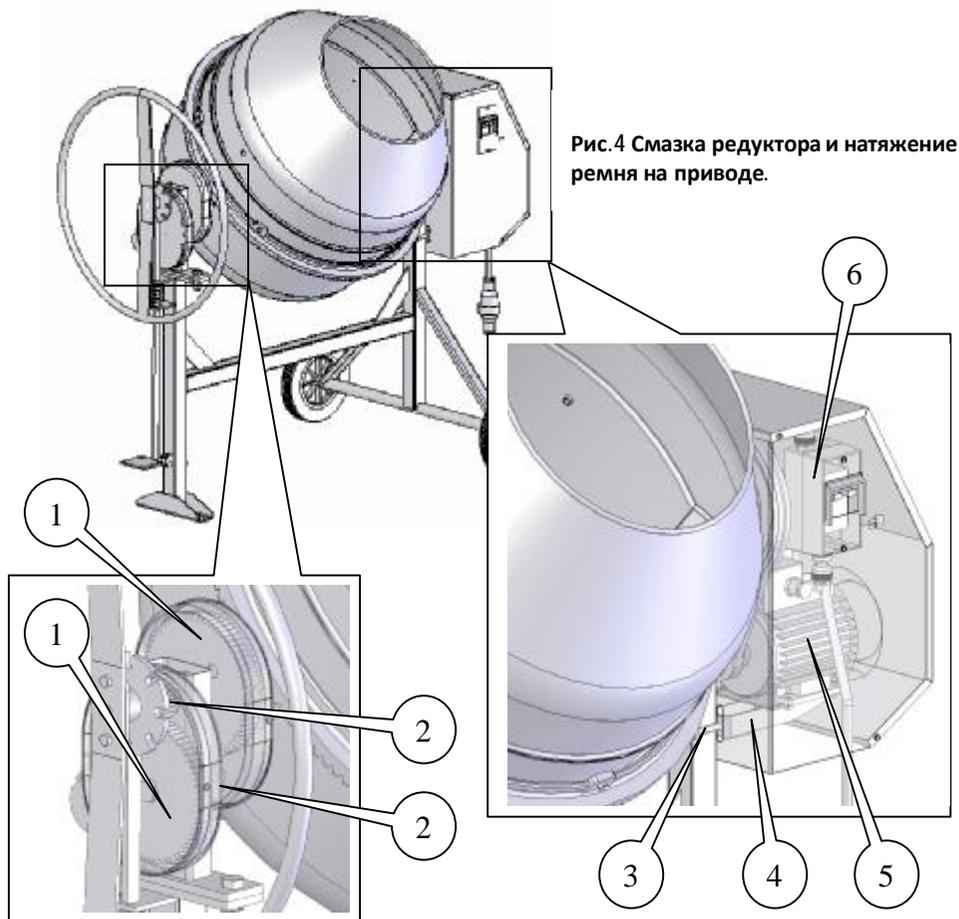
Смазка редуктора и натяжение ремня на приводе.
